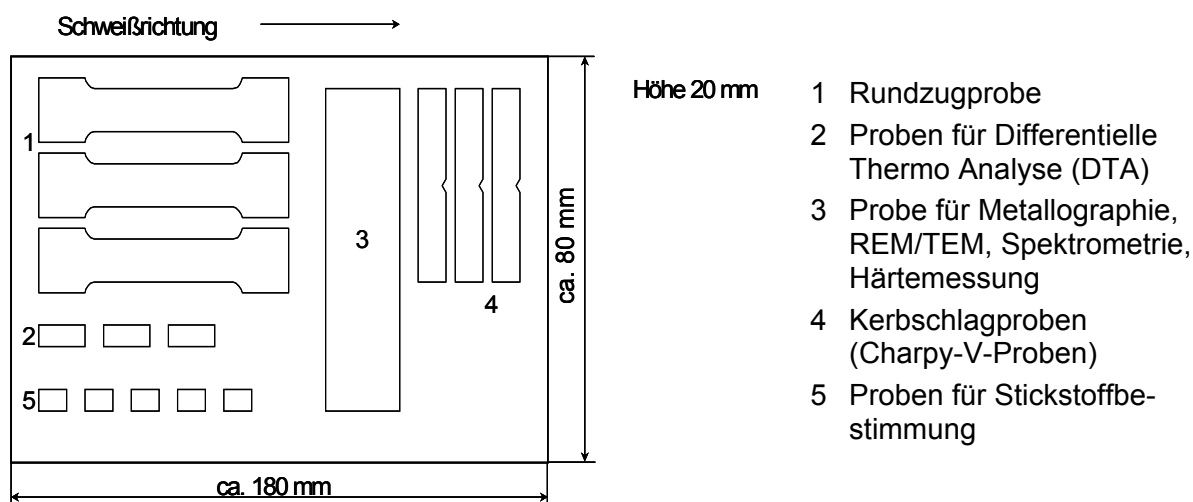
Probenentnahme aus den gefertigten WIG-Schweißgutblöcken
